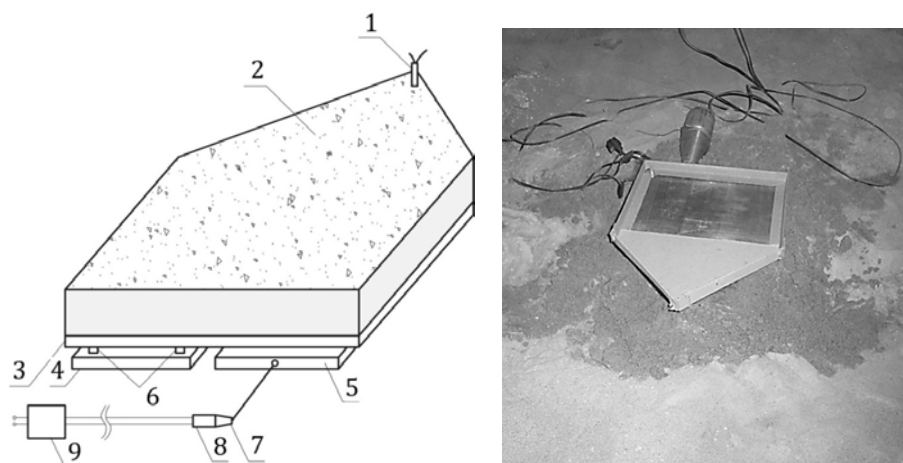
Схема сварки взрывом с воздействием ультразвука:
